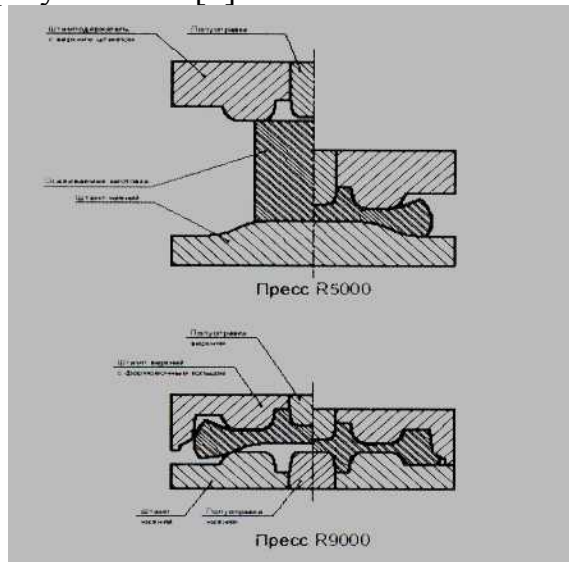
Схема деформирования заготовок железнодорожных колес.
